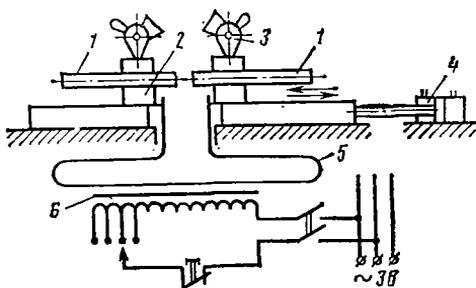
Схема контактной сварки стержневой арматуры
